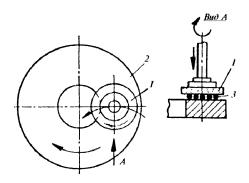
Схема обработки торцов на плоскообдирочном станке:
